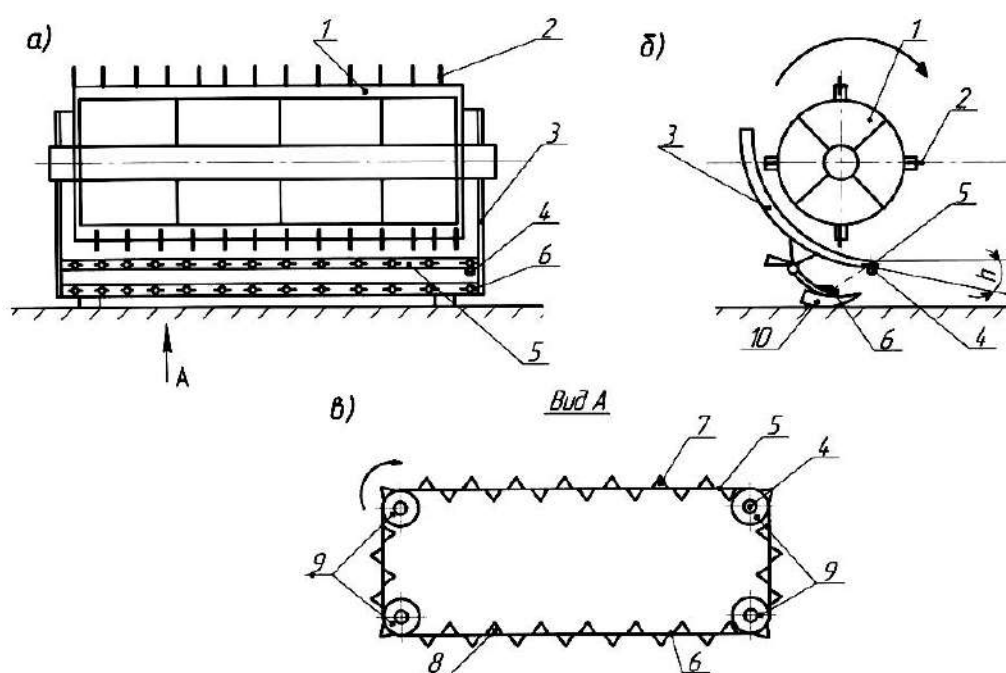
Жатка: а) главный вид; б) вид слева; в) схема конвейера режущего аппарата;
